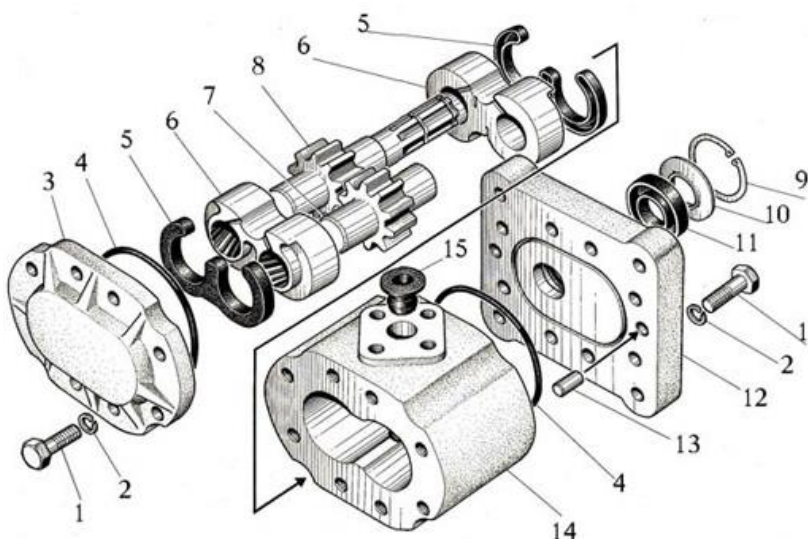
Насос НШ6-3 в разобранном виде: 1-болт; 2-шайба; 3-крышка задняя; 4- кольцо уплотнительное; 5 – манжета фигурная; 6 – подшипник; 7 – шестерня ведомая; 8- шестерня ведущая; 9 – кольцо стопорное; 10 –кольцо опорное; 11 – манжета; 12-крышка передняя; 13- штифт; 14 – корпус; 15 – заглушка транспортная.
